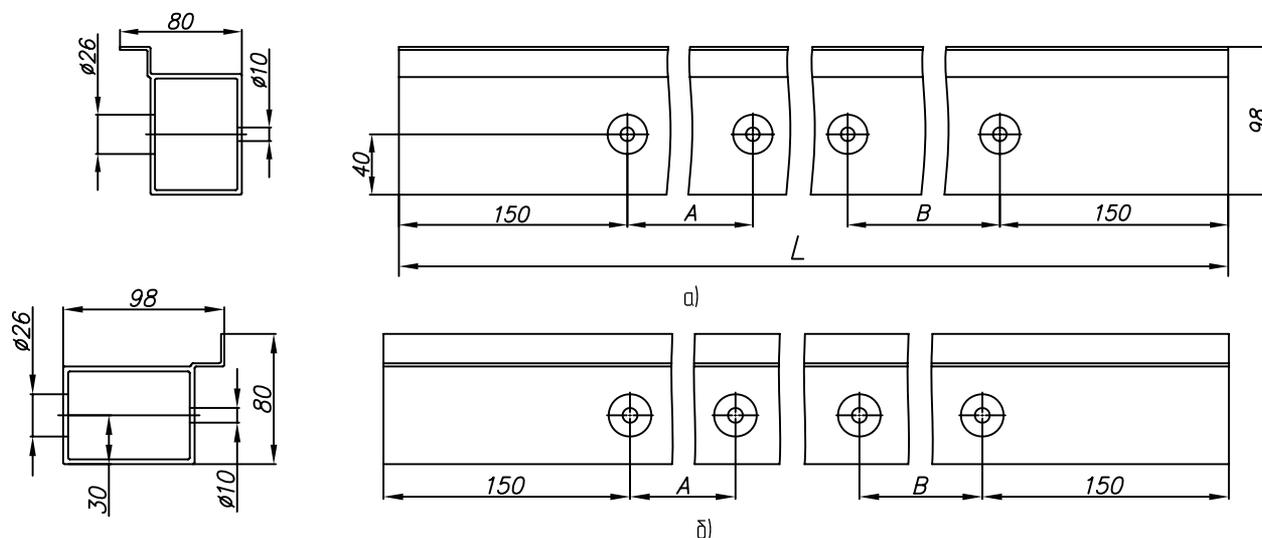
Изготовление столба створки распашных ворот:
